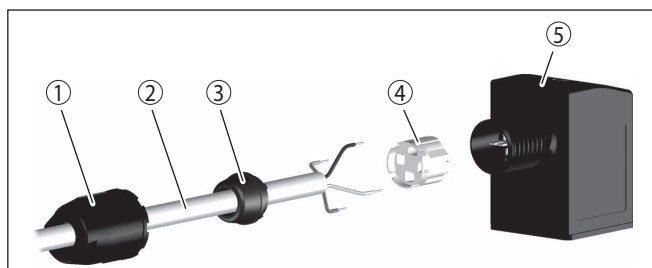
Conexão conector de válvula ISO 4400 com técnica IDC
